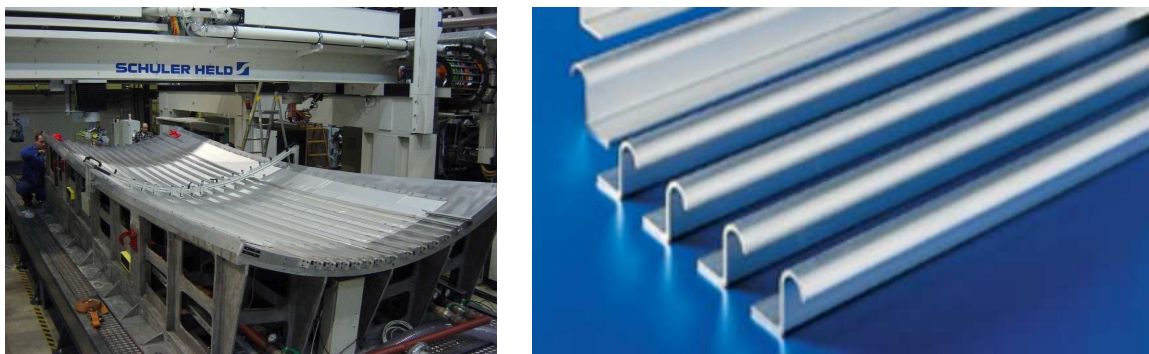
Links: Laserstrahl-Schweißanlage mit sphärischem Rumpfteil und aufgeschweißten Stringern auf einer Schweißstützschale [2]. Rechts: Stringer-Profile aus Aluminium.
